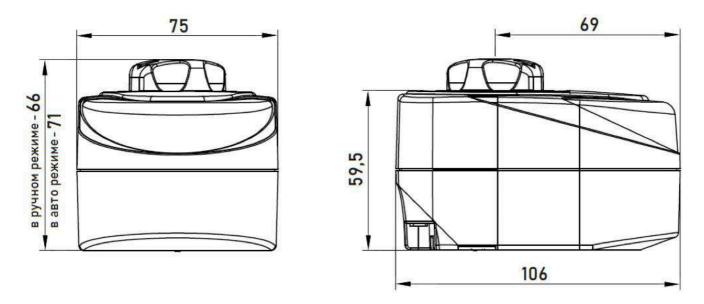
Габаритные размеры сервопривода Standart OKSELER
